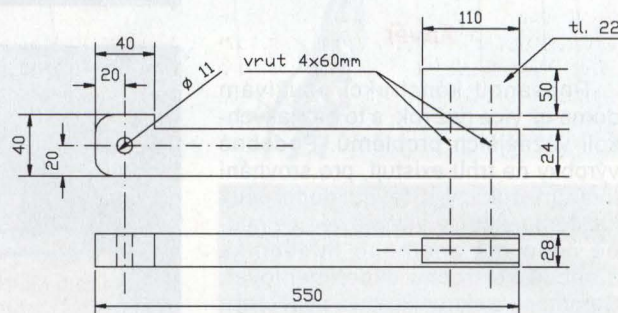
Mechanický díl 4 - uložení čepu (5 ks)
